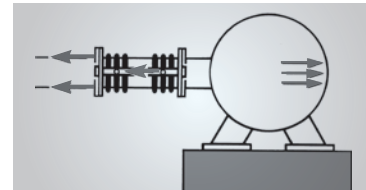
Axialkraft an einem Aggregat mit Lateral-Kompensator
